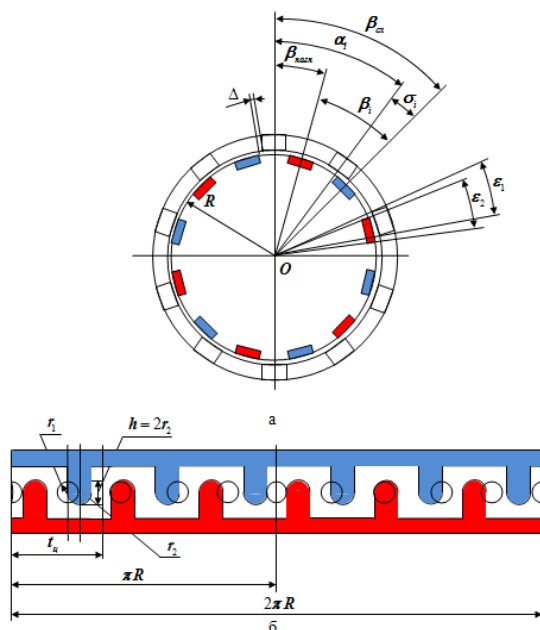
Расчетная схема определения геометрических параметров цапфенной распределительной системы (вала и корпуса) гидромотора планетарного типа ПРГ-7, ПРГ-2:
